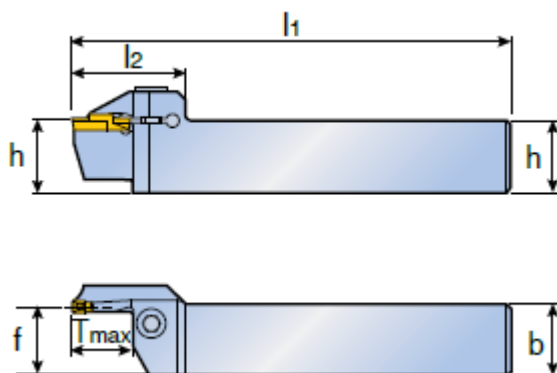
Державка TaeguTec TFR 25-80-5 RN
